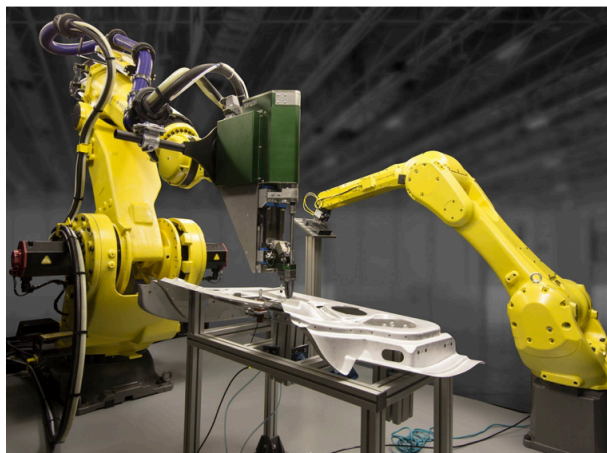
Robot de soldadura por fricción en la automoción. [28]
